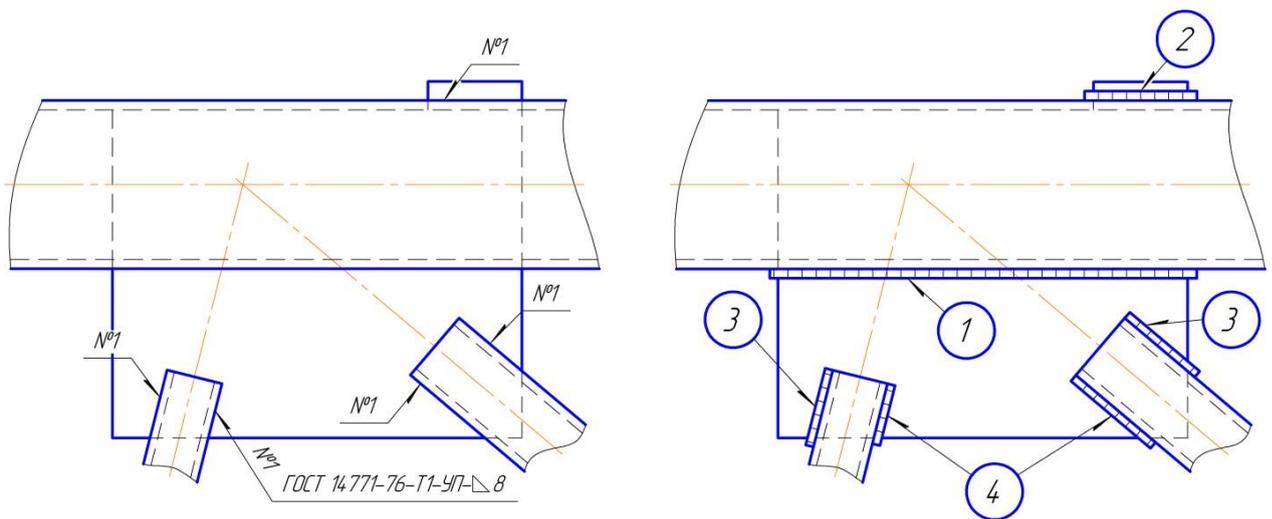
Последовательность наложения сварных швов узла верхнего пояса фермы
